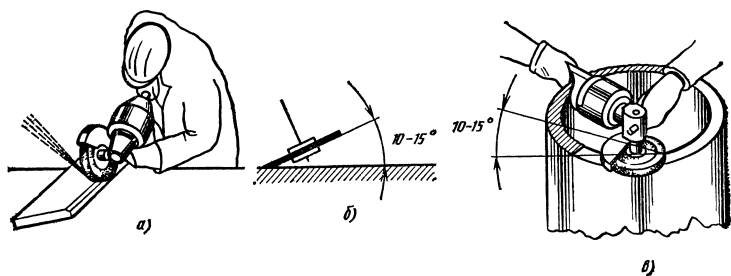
Схемы зачистки фаски под сварку;
